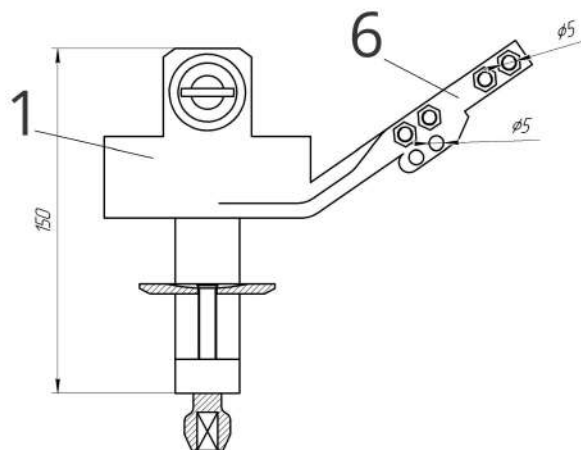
Главный вид устройства для смотки бинта в пауэрлифтинге
